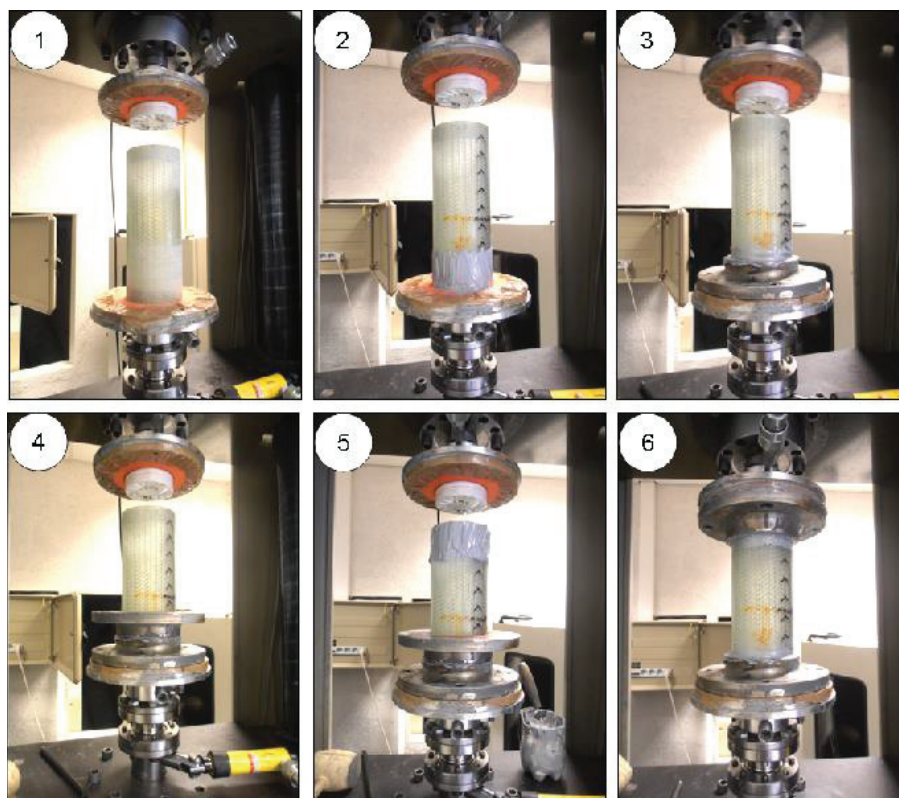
Procédure de collage des pièces de fixation sur l'éprouvette
